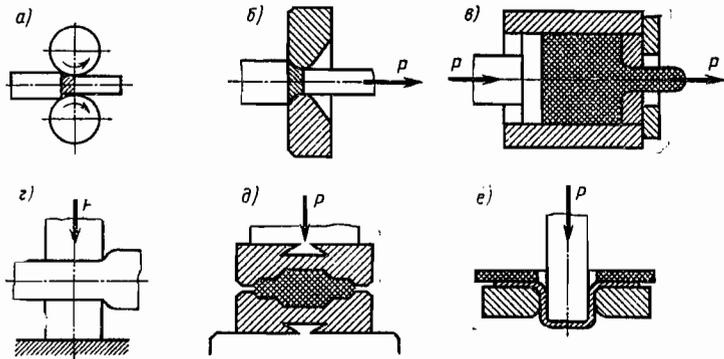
Схема основных способов обработки металлов давлением: а — прокатка; б — волочение; в — прессование; г — ковка; д — объемная штамповка, е — листовая штамповка
